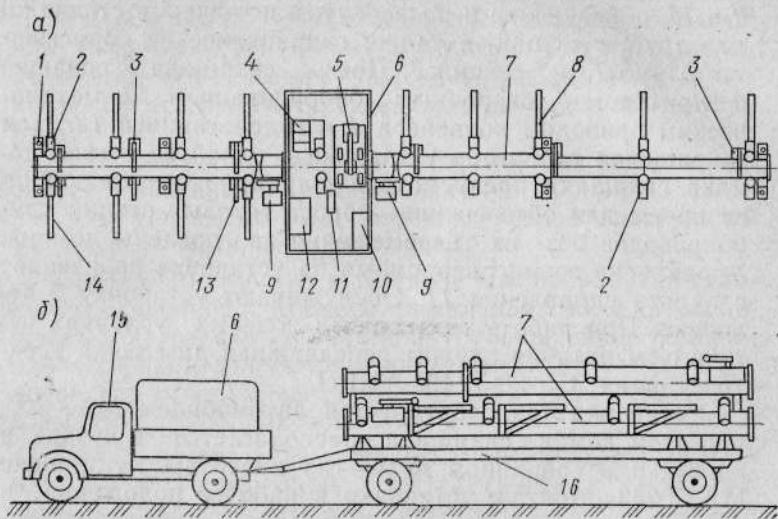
Схема передвижной установки для сборки и сварки секций трубопроводов с  $D_y=80\ldots600$  мм в рабочем *a* и транспортном *b* положении
